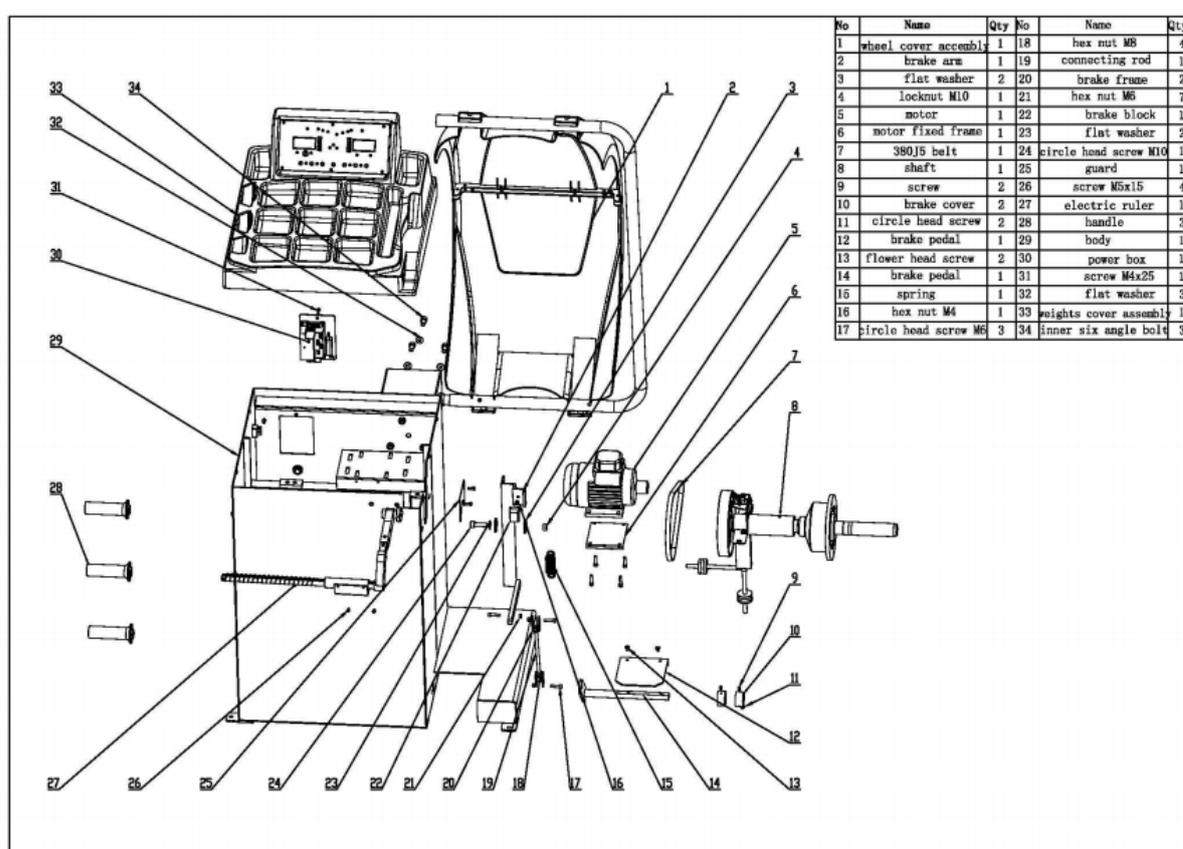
Схема устройства станка для балансировки грузовых колёс NORDBERG ECO 4523C
